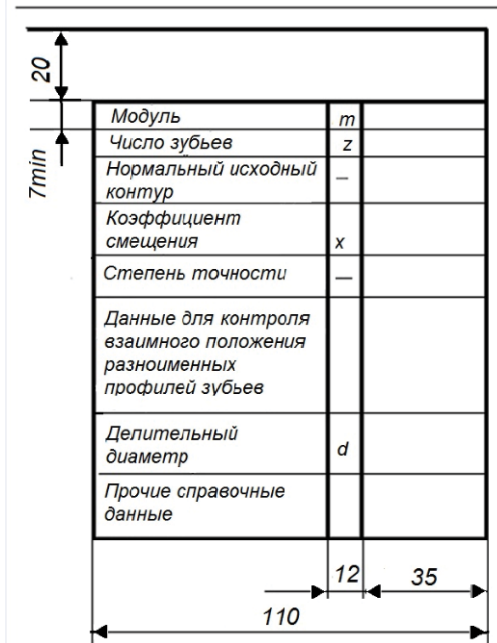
Пример указания параметров зубчатого венца на чертеже прямозубого цилиндрического зубчатого колеса со стандартным исходным контуром
